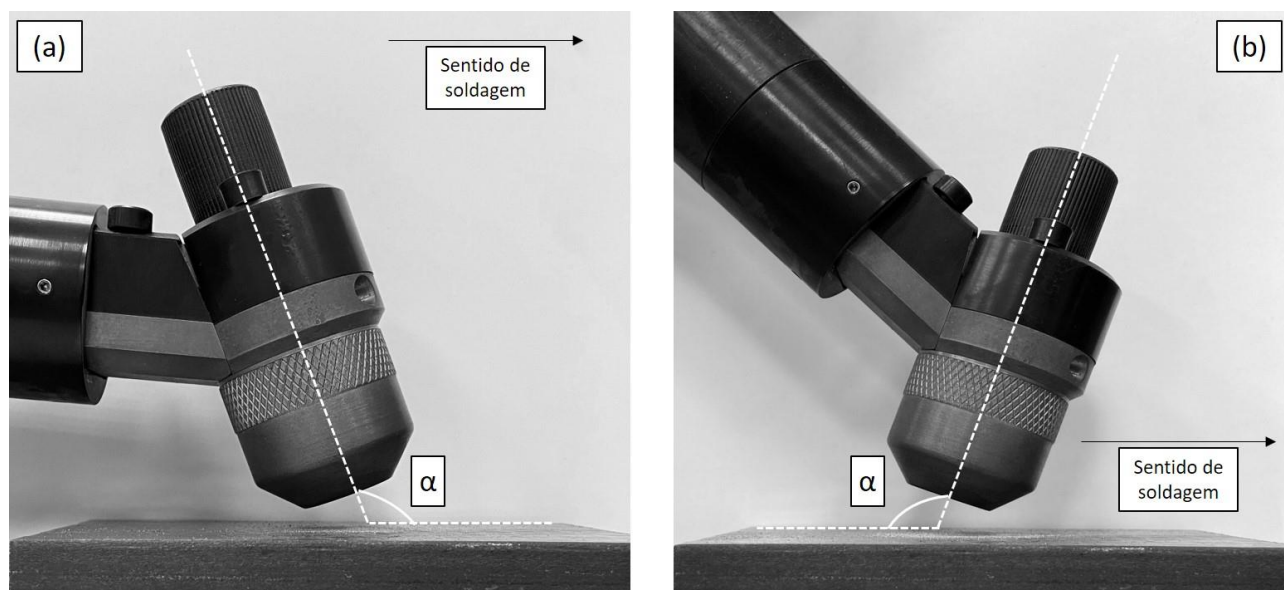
Técnica de avanço da tocha de soldagem PTA-P (a) empurrando e (b) puxando
